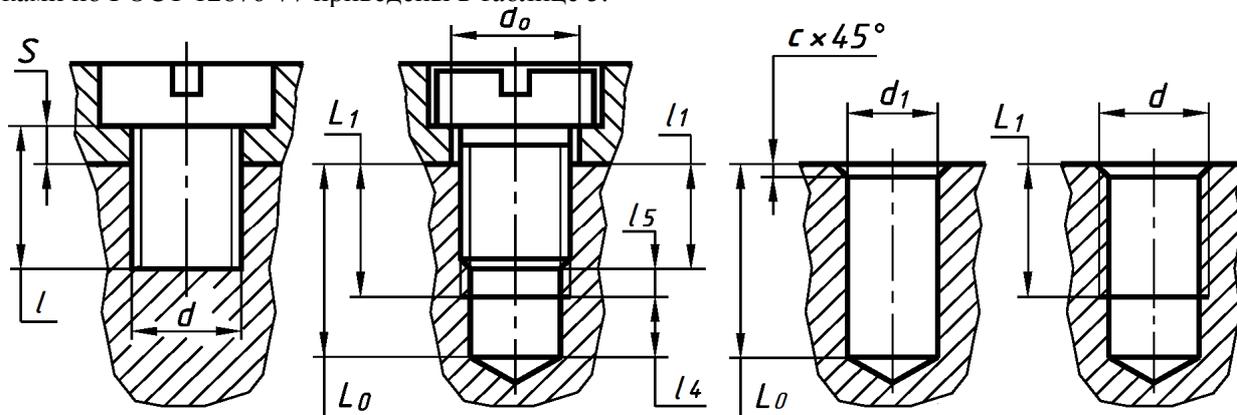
Выходы и запасы резьбы, недорезы для метрических резьб
